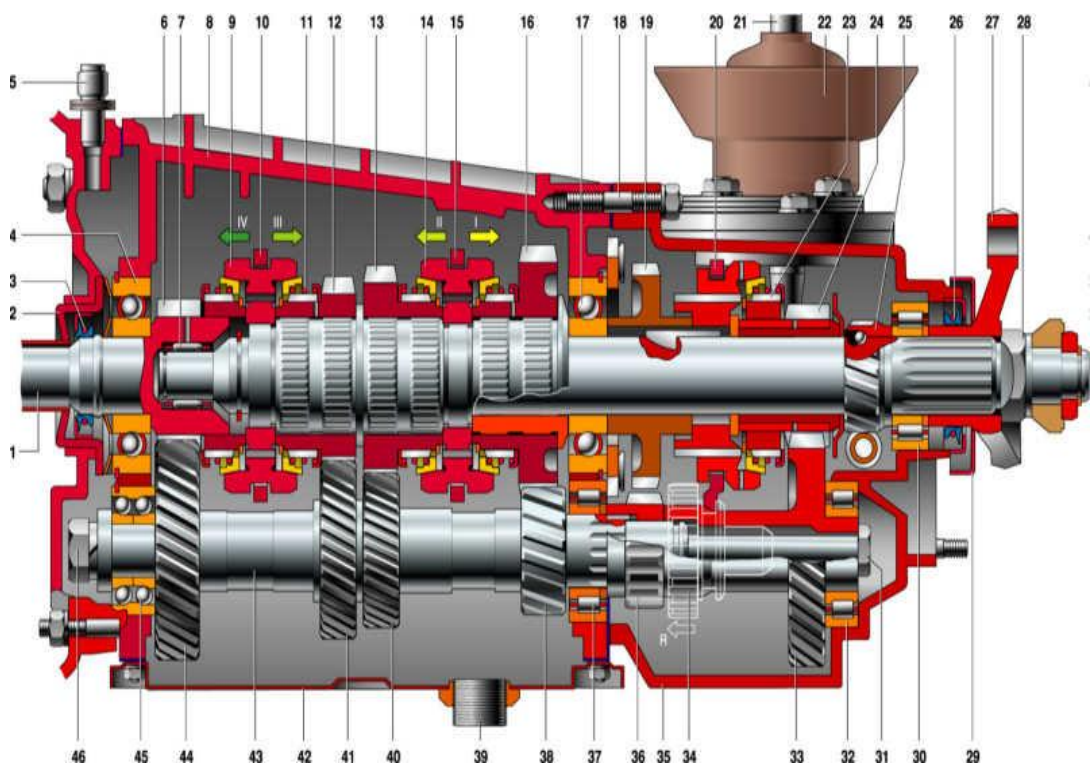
Коробка передач легкового автомобіля BMW
